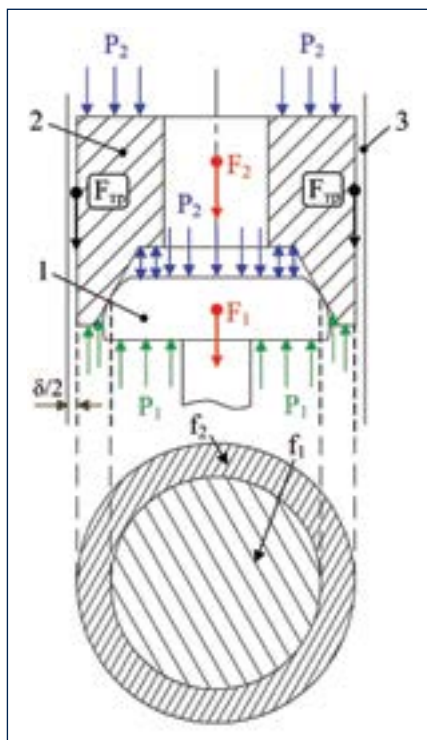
Схема сцепления клапана и плунжера 1 – клапан; 2 – плунжер (седло); 3 – корпус подъемного узла
